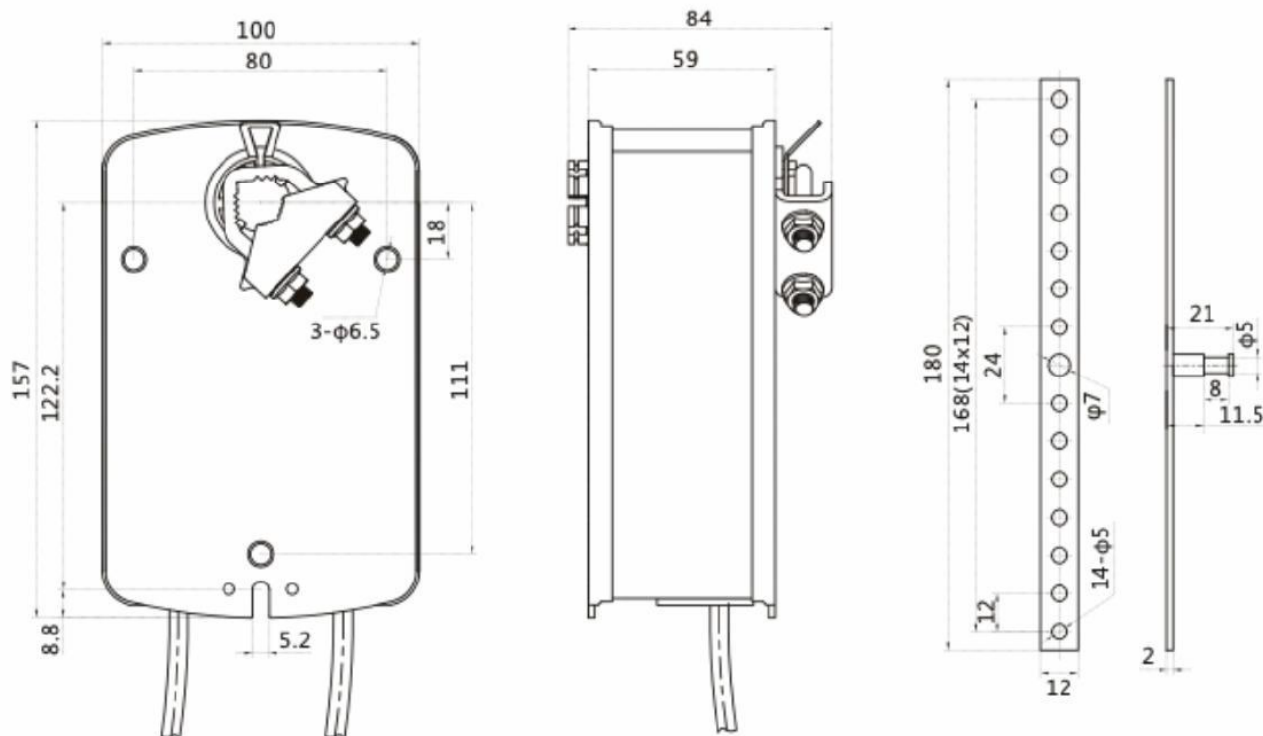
Общий вид и габаритные размеры электропривода VR5WS230-D(DS)
